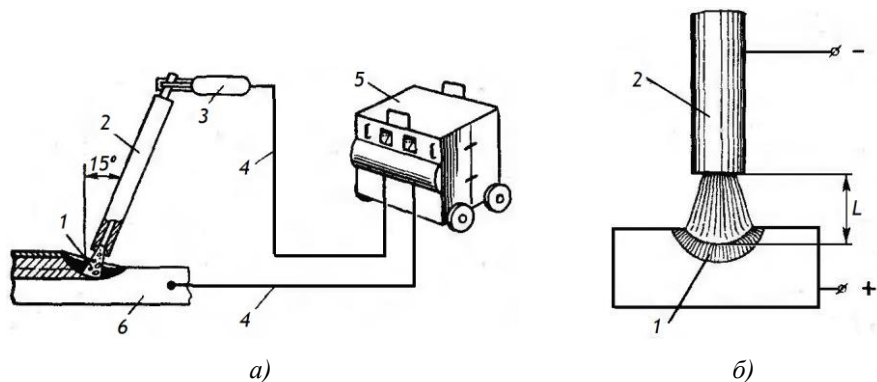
Сварочная электрическая цепь с дугой (а) и сварочная дуга (б), где 1 – сварочная ванна; 2 – электрод; 3 – электродержатель; 4 – провода; 5 – источник питания; 6 – свариваемое изделие; L – длина дуги
